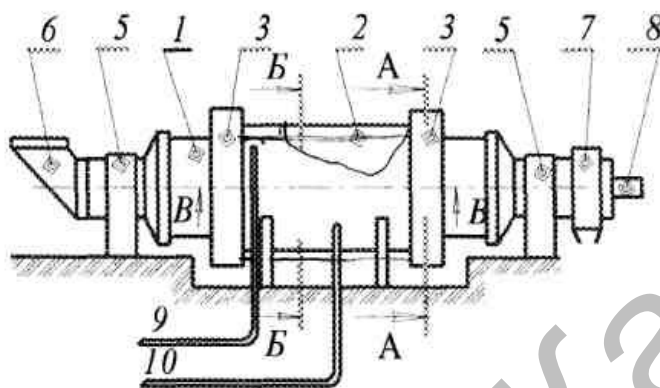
Мельница с устройством разгрузки подшипниковых опор
